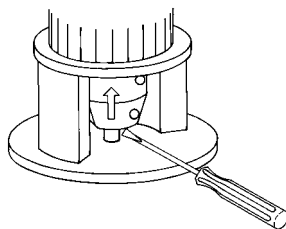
Élévation de l'accouplement et de l'arbre de la pompe
